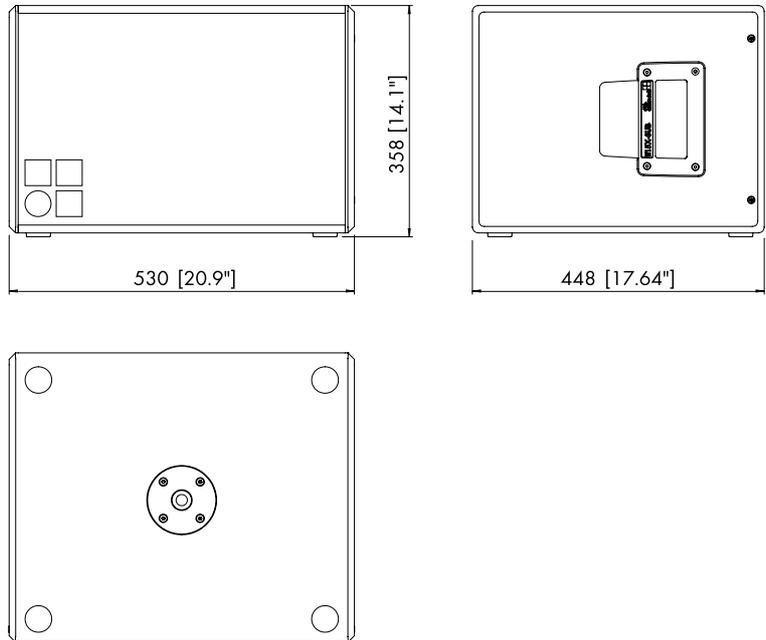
E12X-SUB dimensions du coffre en mm [inch]
